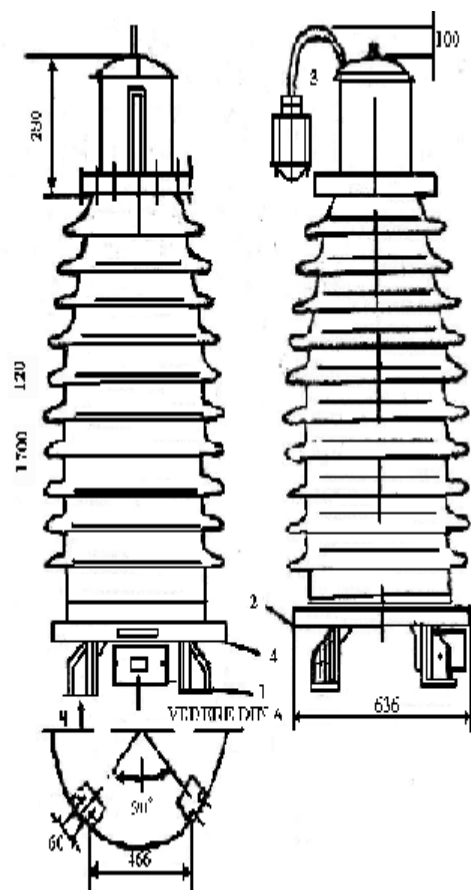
Formă constructivă, dimensiuni și masa TT tip TEMU-110KV , 1- cutie borne secundare; 2- clemă legare la pământ; 3- bornă primară M16; 4-eticheta
